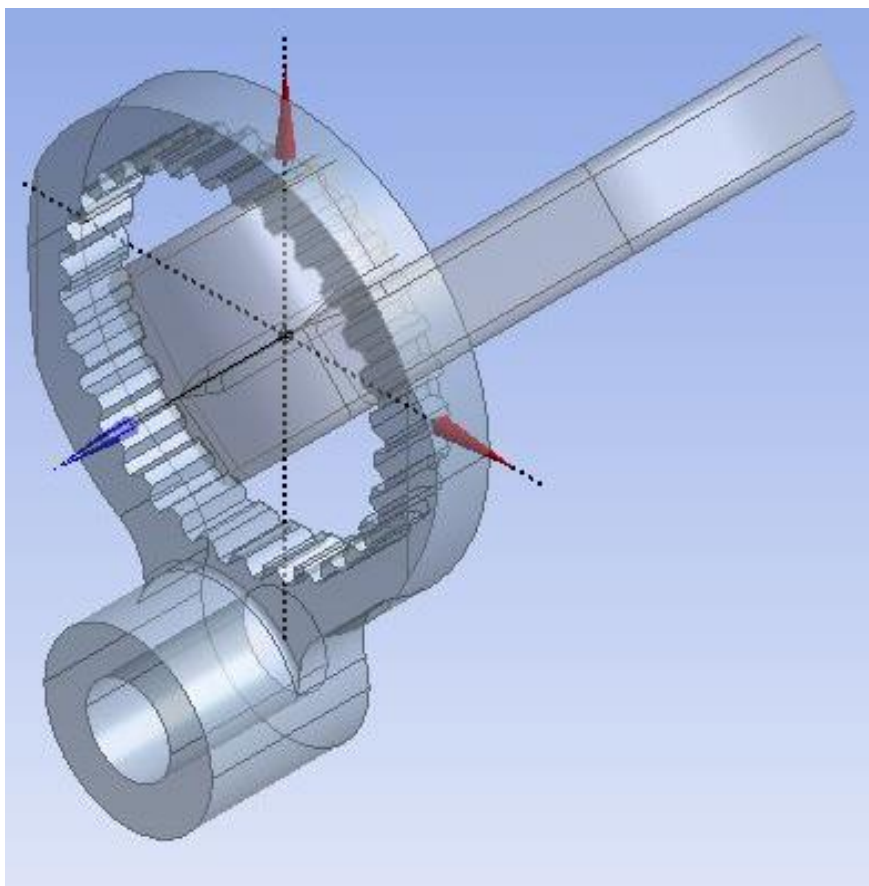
Початкове розташування CAD-моделей заготовки та деталі в тестовій задачі
